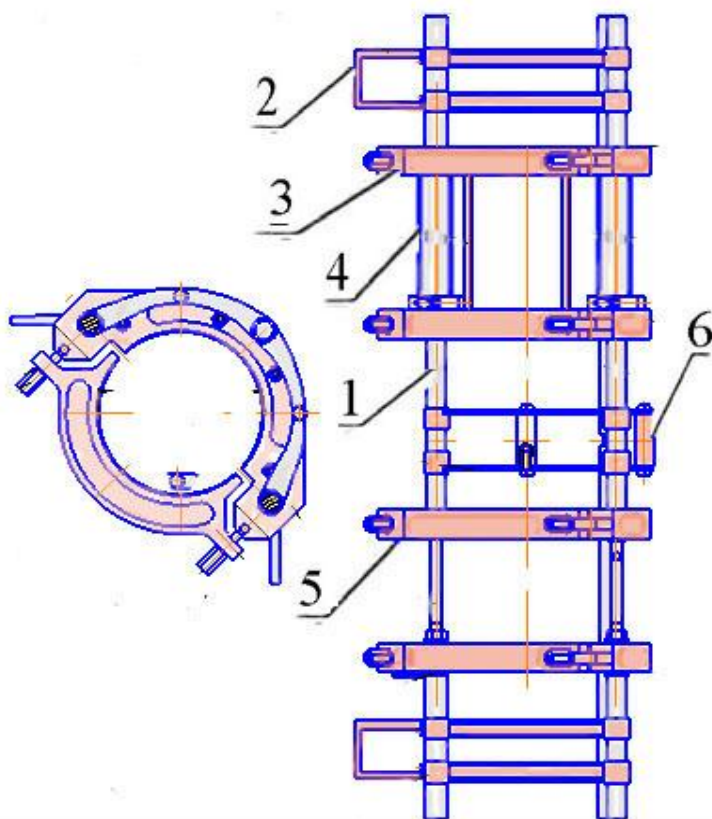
Устройство центратора установки для сварки полиэтиленовых труб с вертикальным расположением осей
